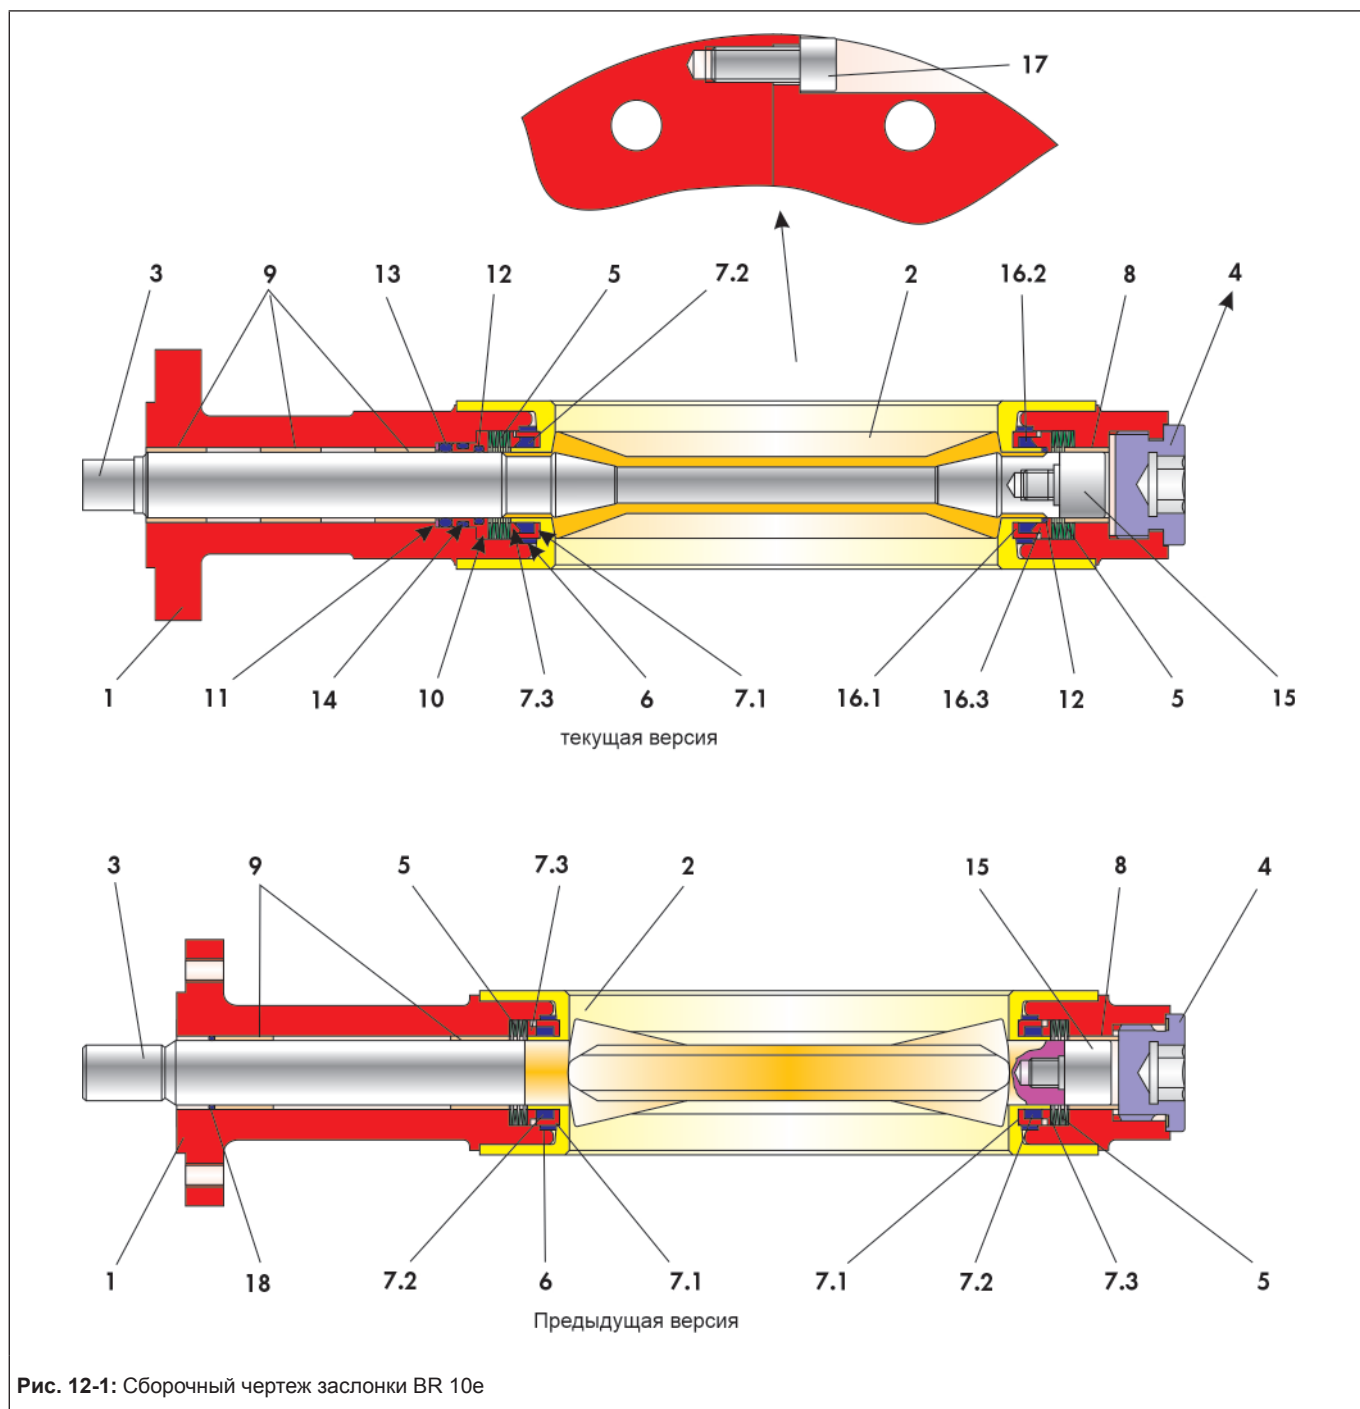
Сборочный чертеж заслонки BR 10e
